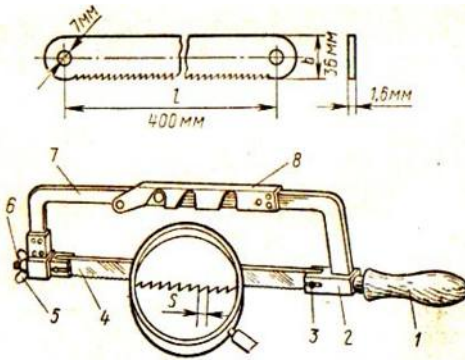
Ручная ножовка: полотно; ножовка в сборе
